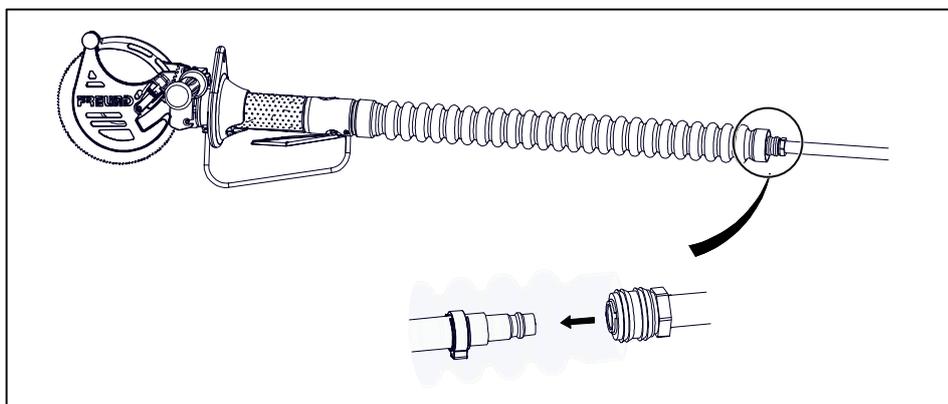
Raccordement de la machine K16-P4\_evo2
